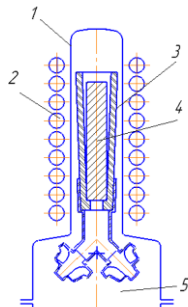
Бестигельное вакуумное индукционное устройство с индуктором, расположенным вне вакуумного пространства 1 — плавильная камера (колба); 2 — индуктор; 3 — форма; 4 — мерная заготовка; 5 — заливочная камера
